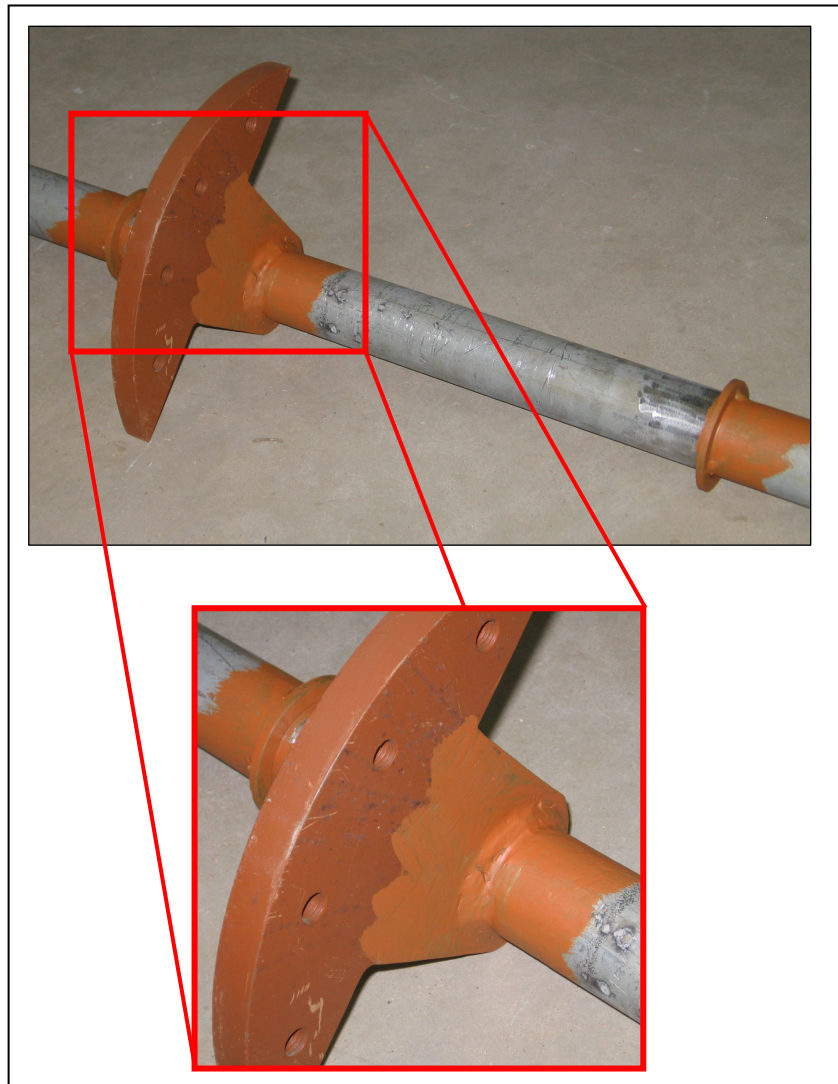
Soldagem realizada no Laboratório de Soldagem e Materiais – LASOMET/CT/UFSM.
